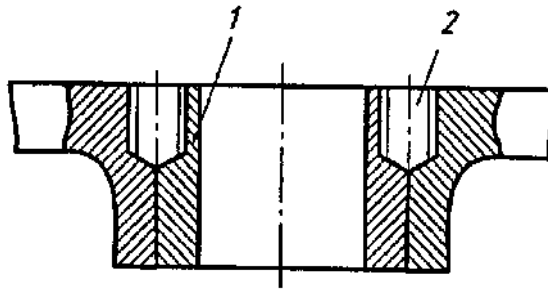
Фрагмента подшипникового щита с восстановленной посадочной поверхностью под подшипник: 1 – втулка; 2 – стопор
